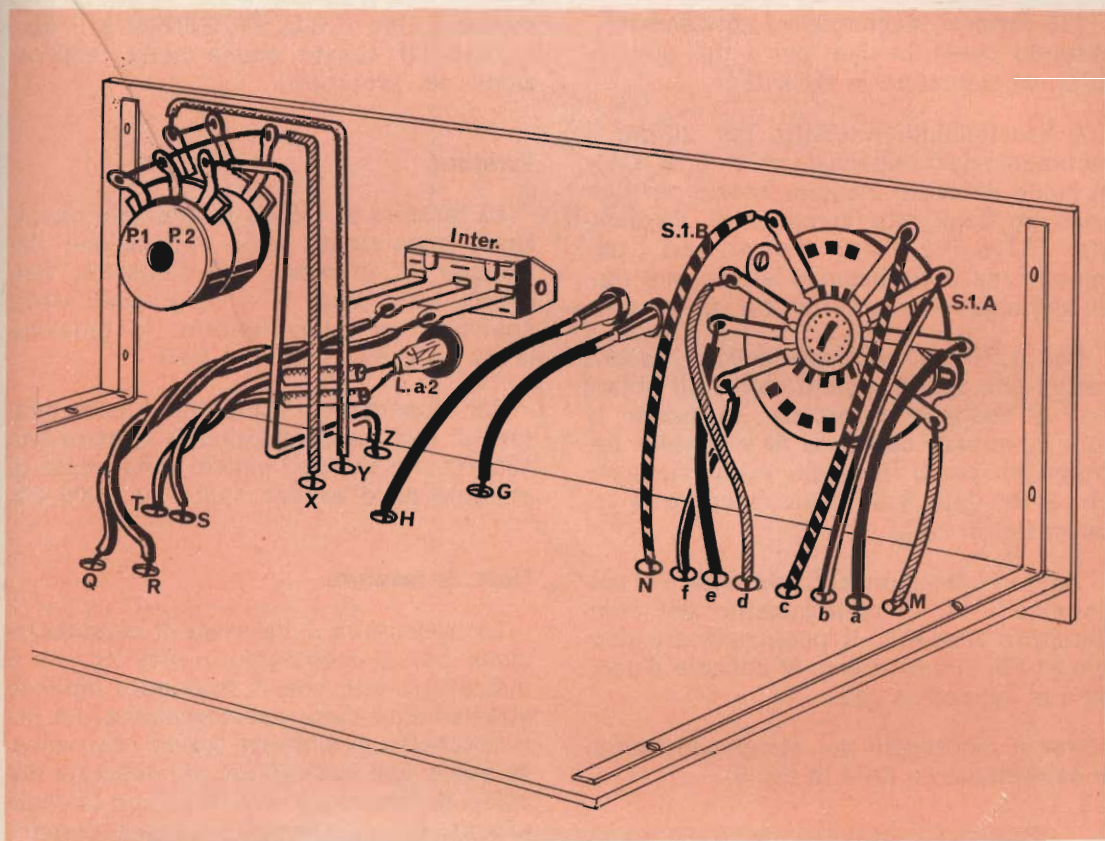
Schema di montaggio dei componenti sul pannello frontale.
